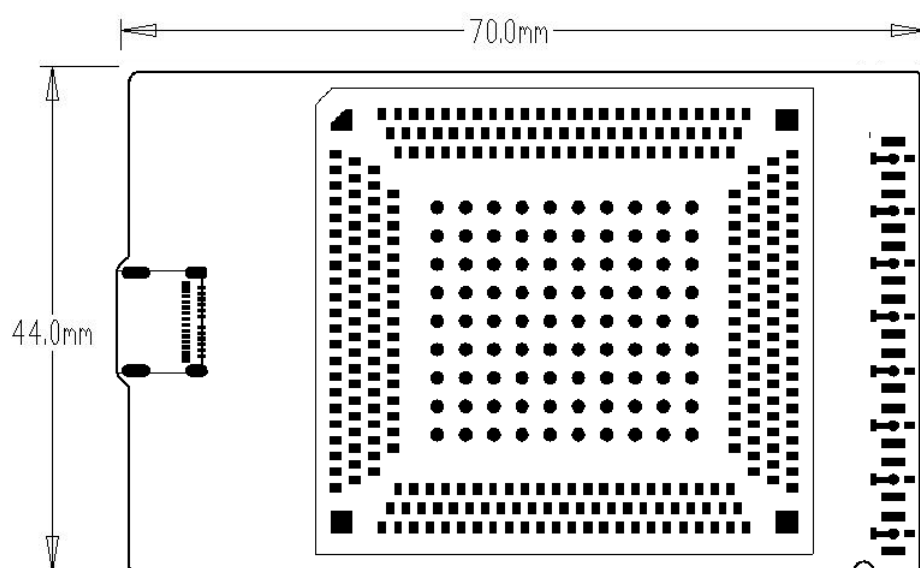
SLA4470 模组 PCB 布局和尺寸（单位：mm）
